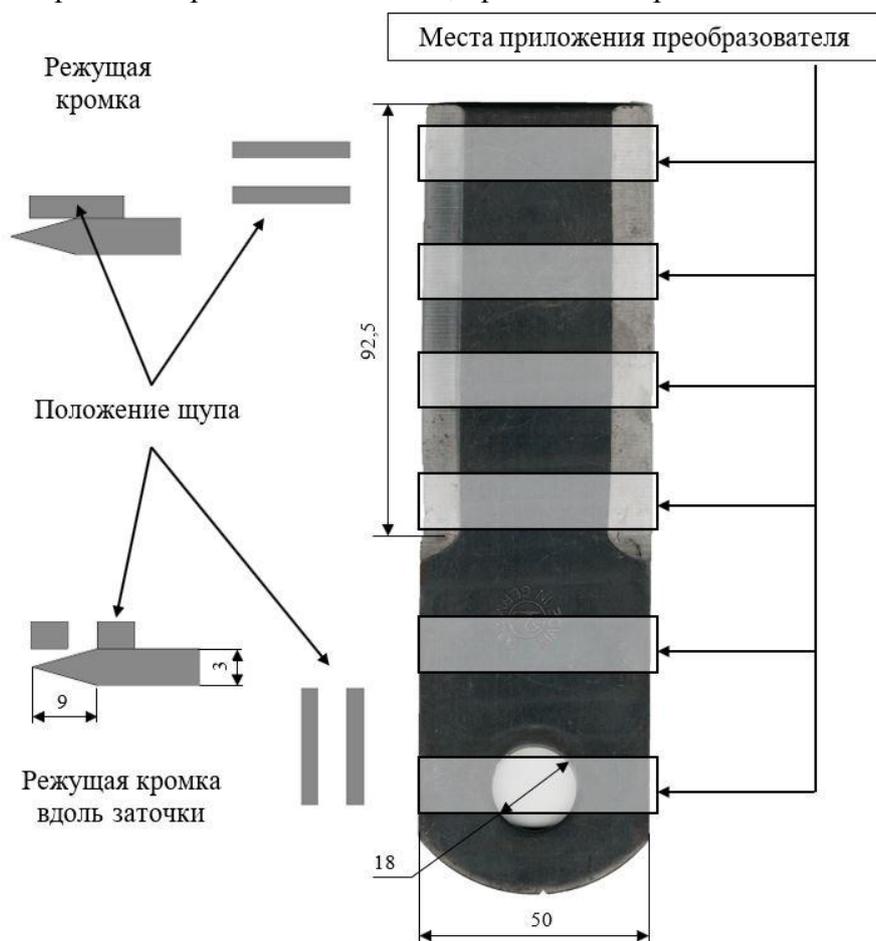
Схема измерений коэрцитивной силы ножа ротора
